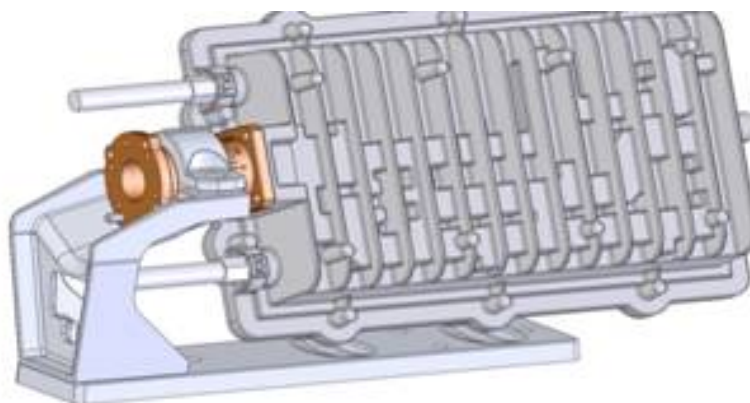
Общий вид приёмопередатчика ODU-2W-KU с опорной рамой
